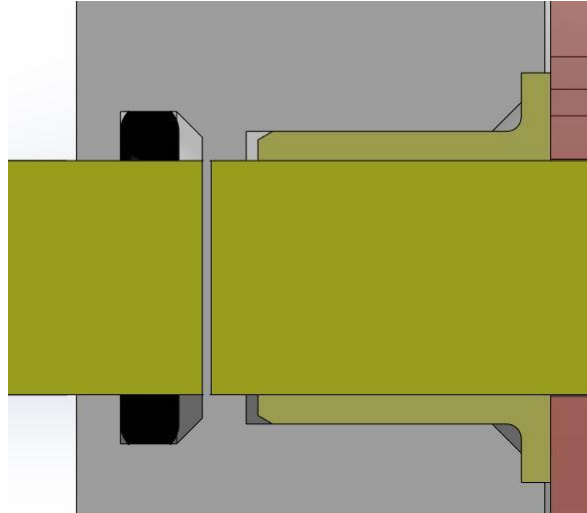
Vista de secció del model CAD de la junta estanca (Font pròpia)
